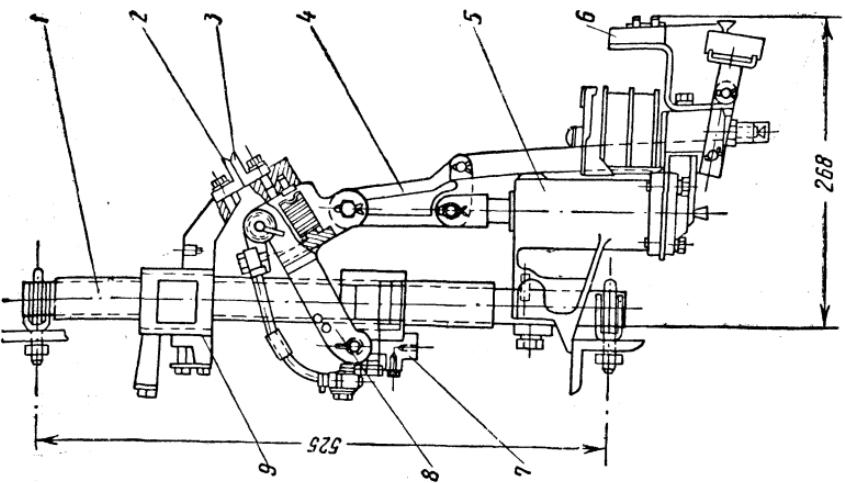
Электропневматический контактор типа ПК-06-11:
